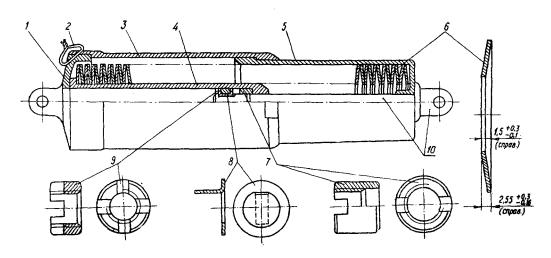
Пружинный амортизатор Ш4700-20 лыжонка: I — крышка Ш4700-21; 2 — проволока контровочная KO-1,0 (шплинт 1,5 \times 15); 3 — цилиндр Ш4700-22; 4 — шток Ш4700-23; 5 — поршень Ш4700-27; 6 — пружины тарельчатые Ш4700-28; 7 — гайка Ш4700-25; 8 — шайба контровочная Ш4700-33; 9 — гайка Ш4700-31; 10 — шток Ш4700-32
